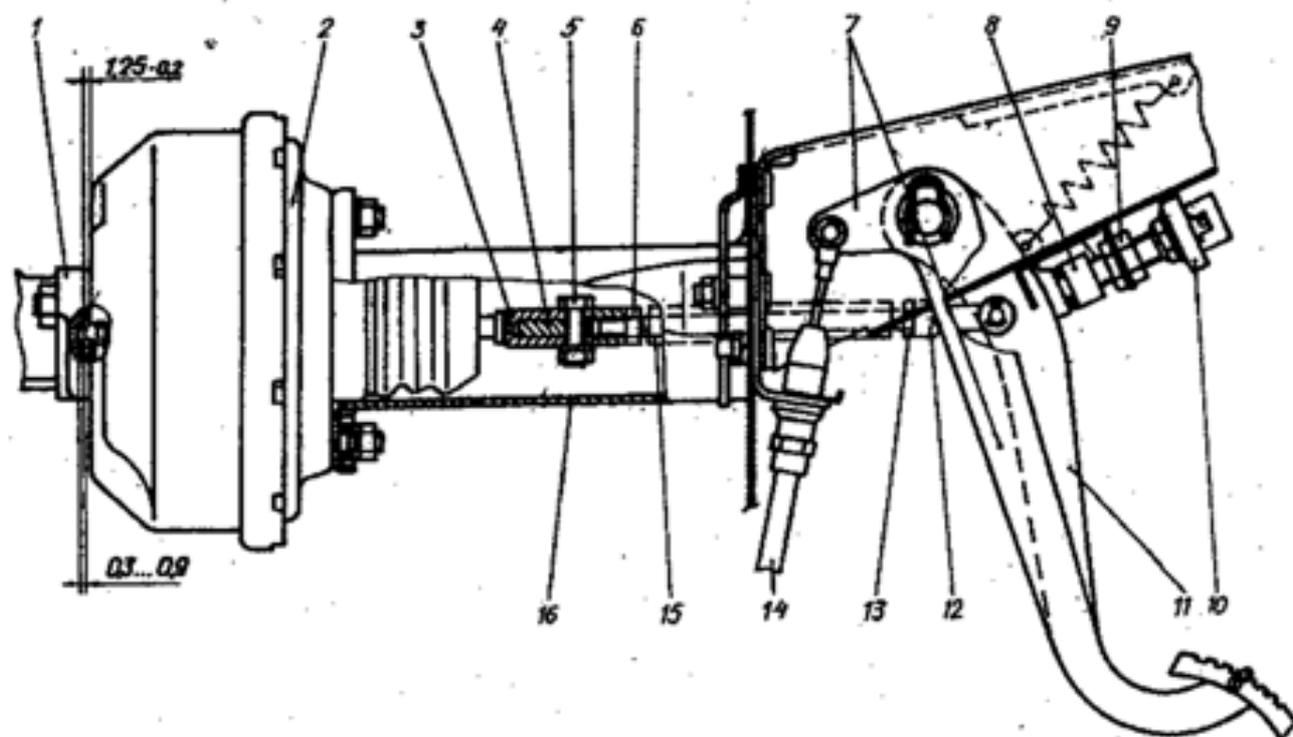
Гидропривод тормоза ножного с вакуумным усилителем: 1 - главный тормозной цилиндр в сборе; 2 - усилитель тормозов вакуумный; 3 - вилка штока вакуумного усилителя; 4 - соединитель; 5 - болт; 6 - контргайка; 7 - педаль сцепления; 8 - наконечник; 9 - контргайка; 10 - выключатель стоп-сигнала; 11 - педаль тормоза; 12 - вилка толкателя; 13 - контргайка; 14 - трос сцепления; 15 - толкатель; 16 - кромштейн вакуумного усилителя.
